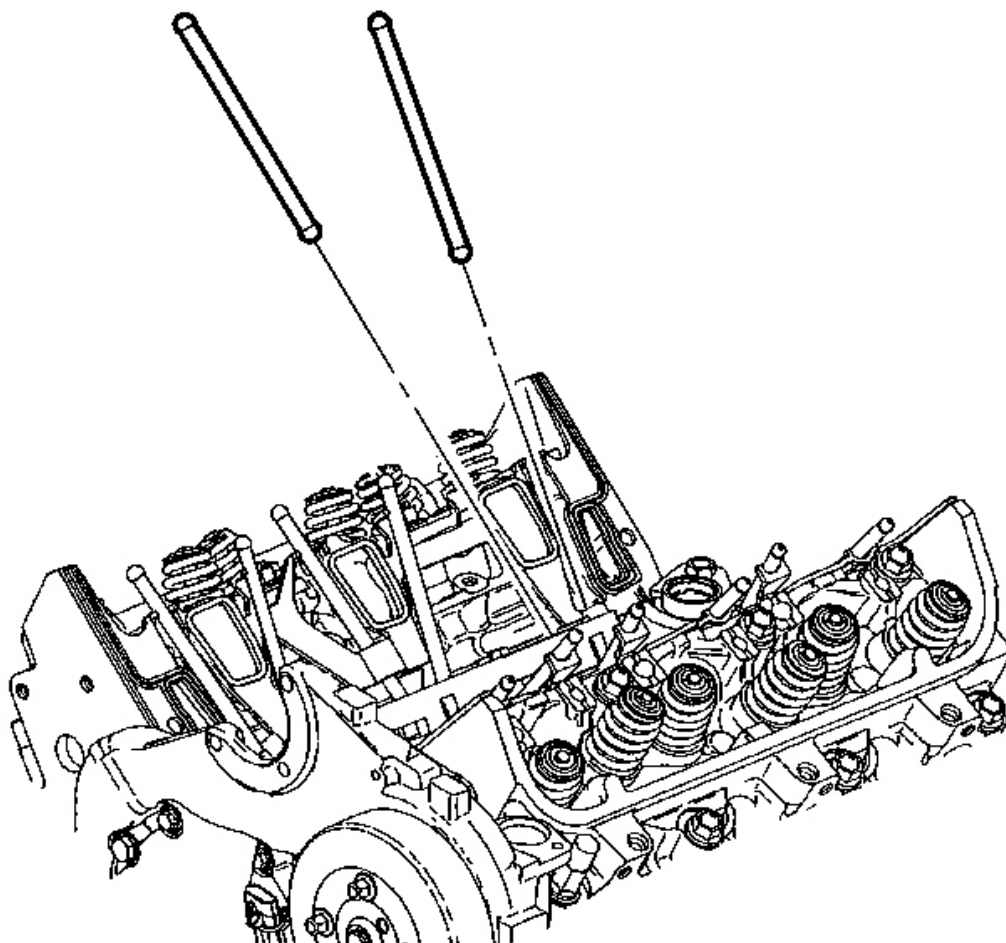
Vista de la válvula Cortesía de balancines de General Motors Corp.
